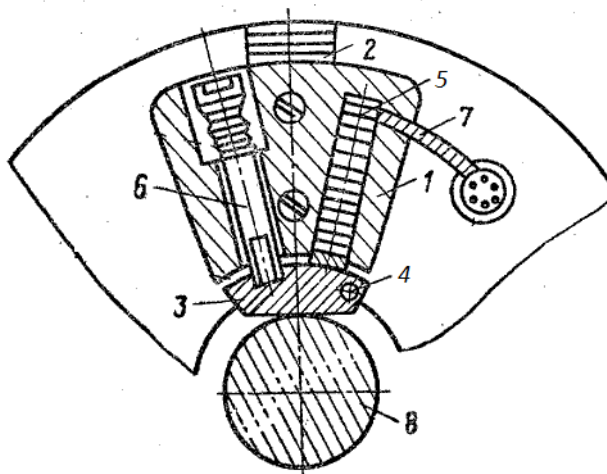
Кулачки с механизмом автоматической поднастройки положения оси заготовки
